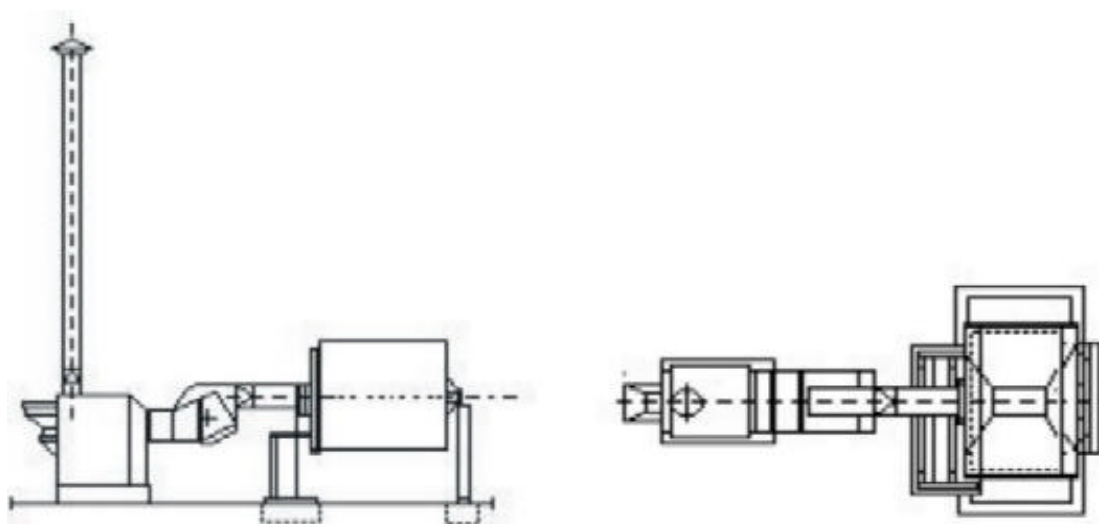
Croqui: vista lateral e superior do conjunto fornalha-secador rotativo.
